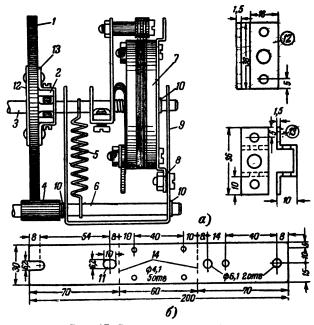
Верньерное устройство. a — общий вид; δ — разметка стойки.
